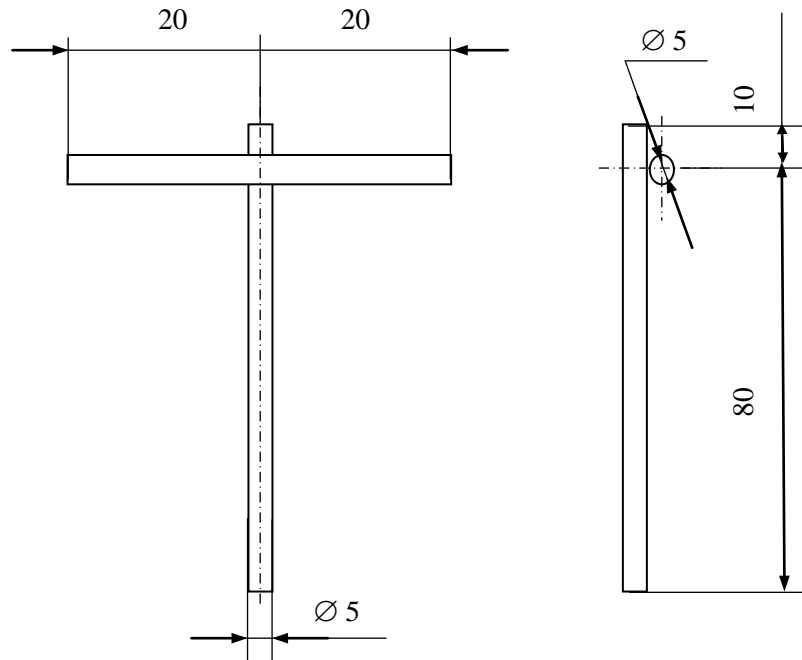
Образец для сварки (элемент металлической сетки)
